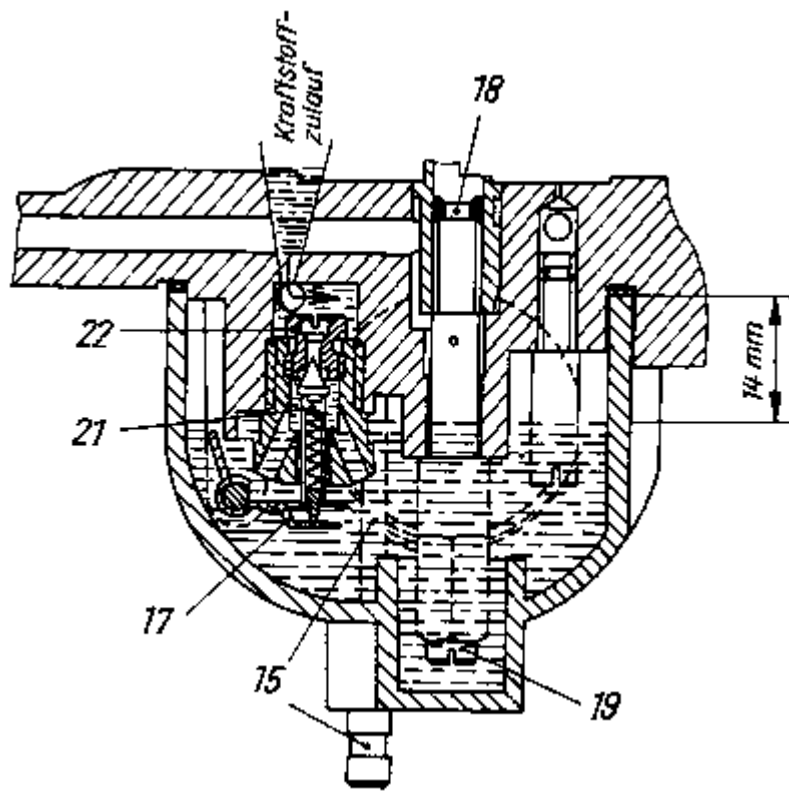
Vergaserunterteil (Schnittzeichnung) Kraftstoffniveau
